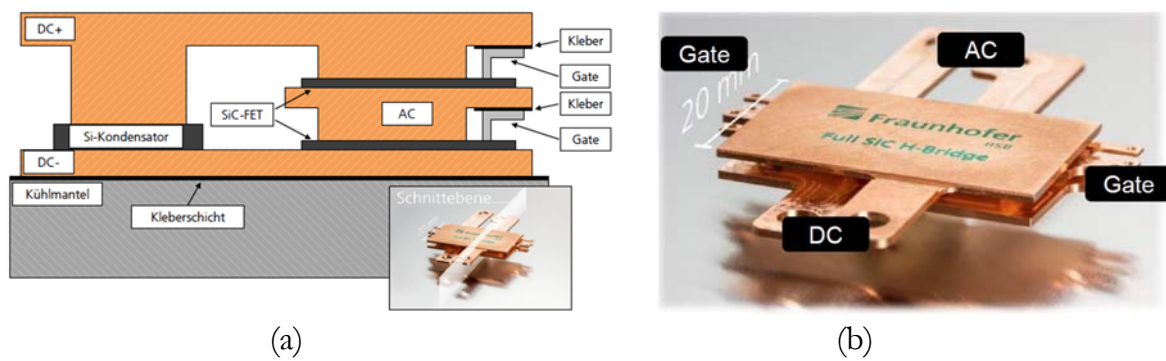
vue en coupe de l'assemblage et (b) module réalisé [35]
